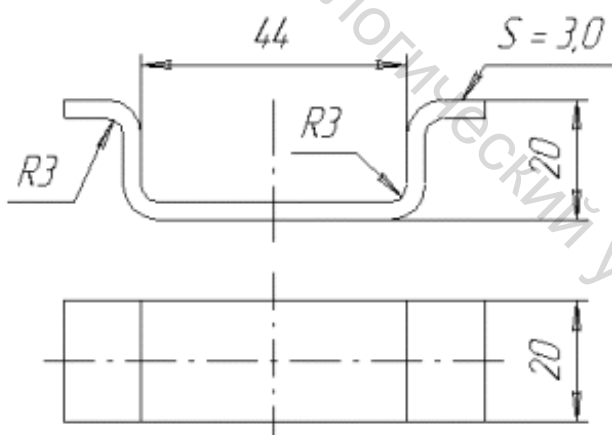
Эскиз детали для проектирования гибочного штампа
